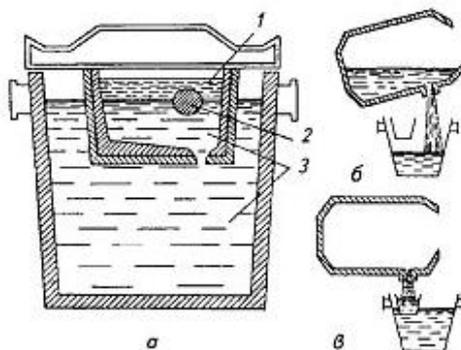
Схема отделения шлака от металла с использованием промежуточной емкости: а – разрез сталеразливочного ковша и промежуточной емкости в момент окончания выпуска; б – начало выпуска; в – окончание выпуска; 1 – шлак; 2 – плавающий шар – отсекающий шлака; 3 – металл
